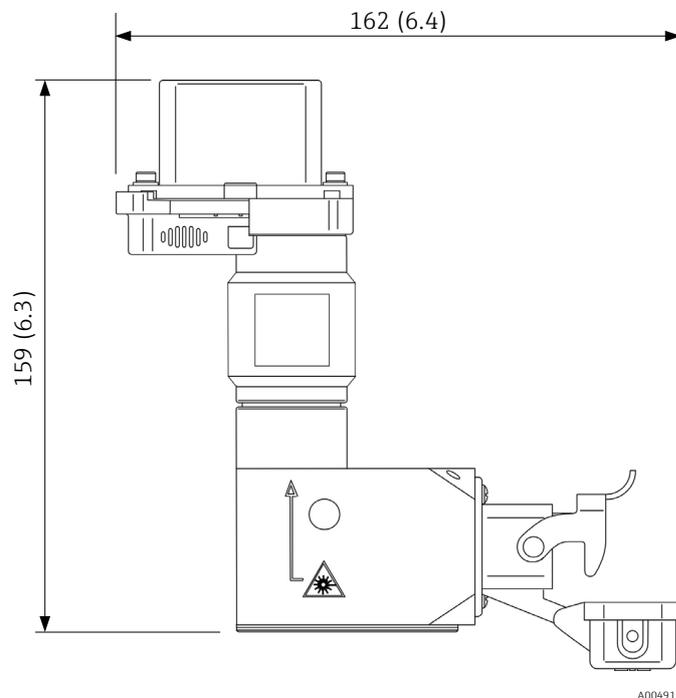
Vue de côté de la sonde Rxn-46. Dimensions : mm (in)
